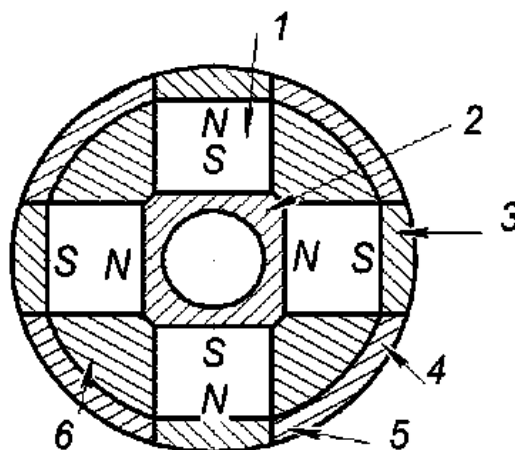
Конструкция ротора звездообразного типа с полюсными башмаками.
